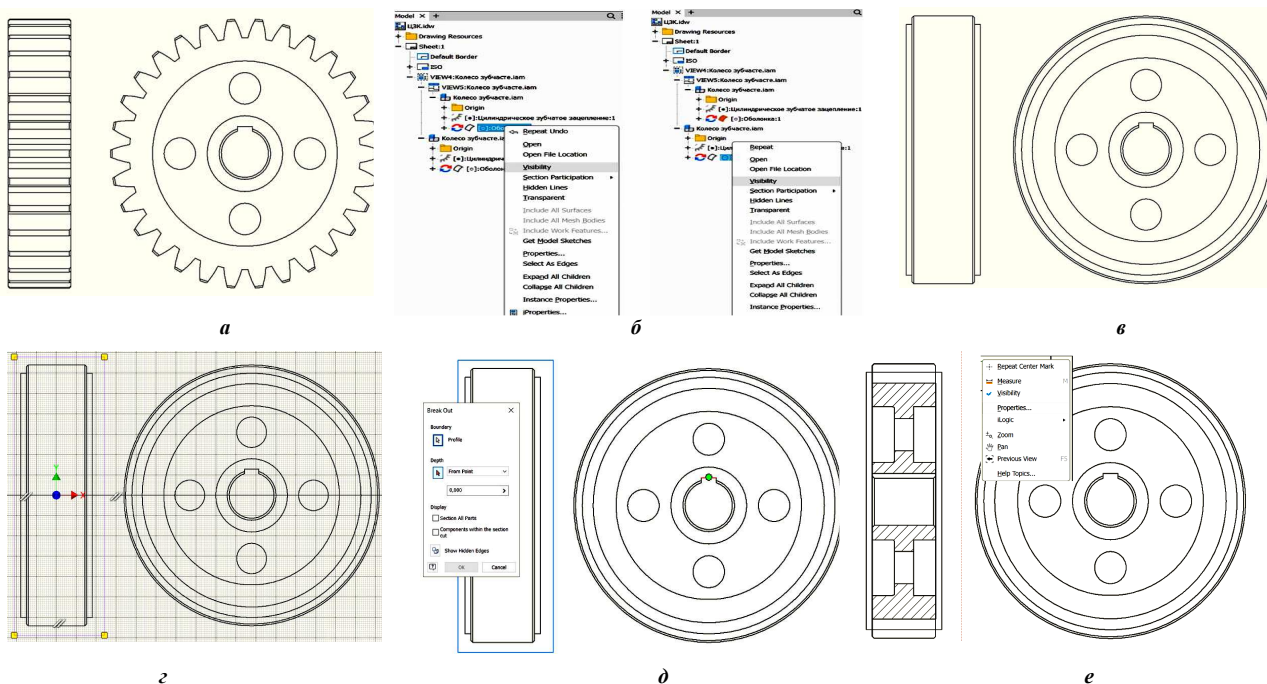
Алгоритм редагування видів циліндричного зубчастого колеса
